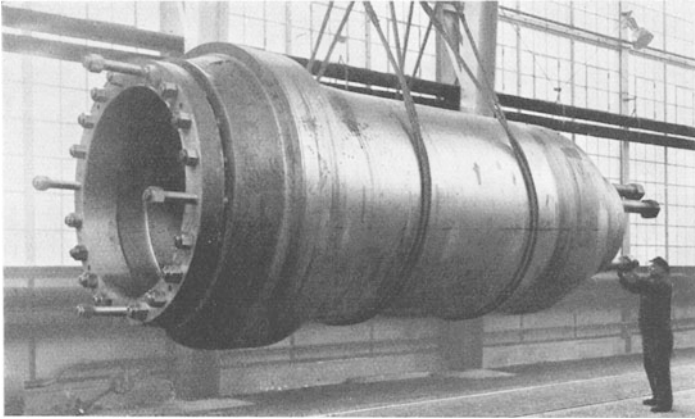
Hohlgeschmiedeter Preßzylinder. Länge 5000 mm, größter Außendurchmesser 2250 mm, Gewicht etwa 50000 kg. (Hydraulik G. m. b. H., Duisburg.)
